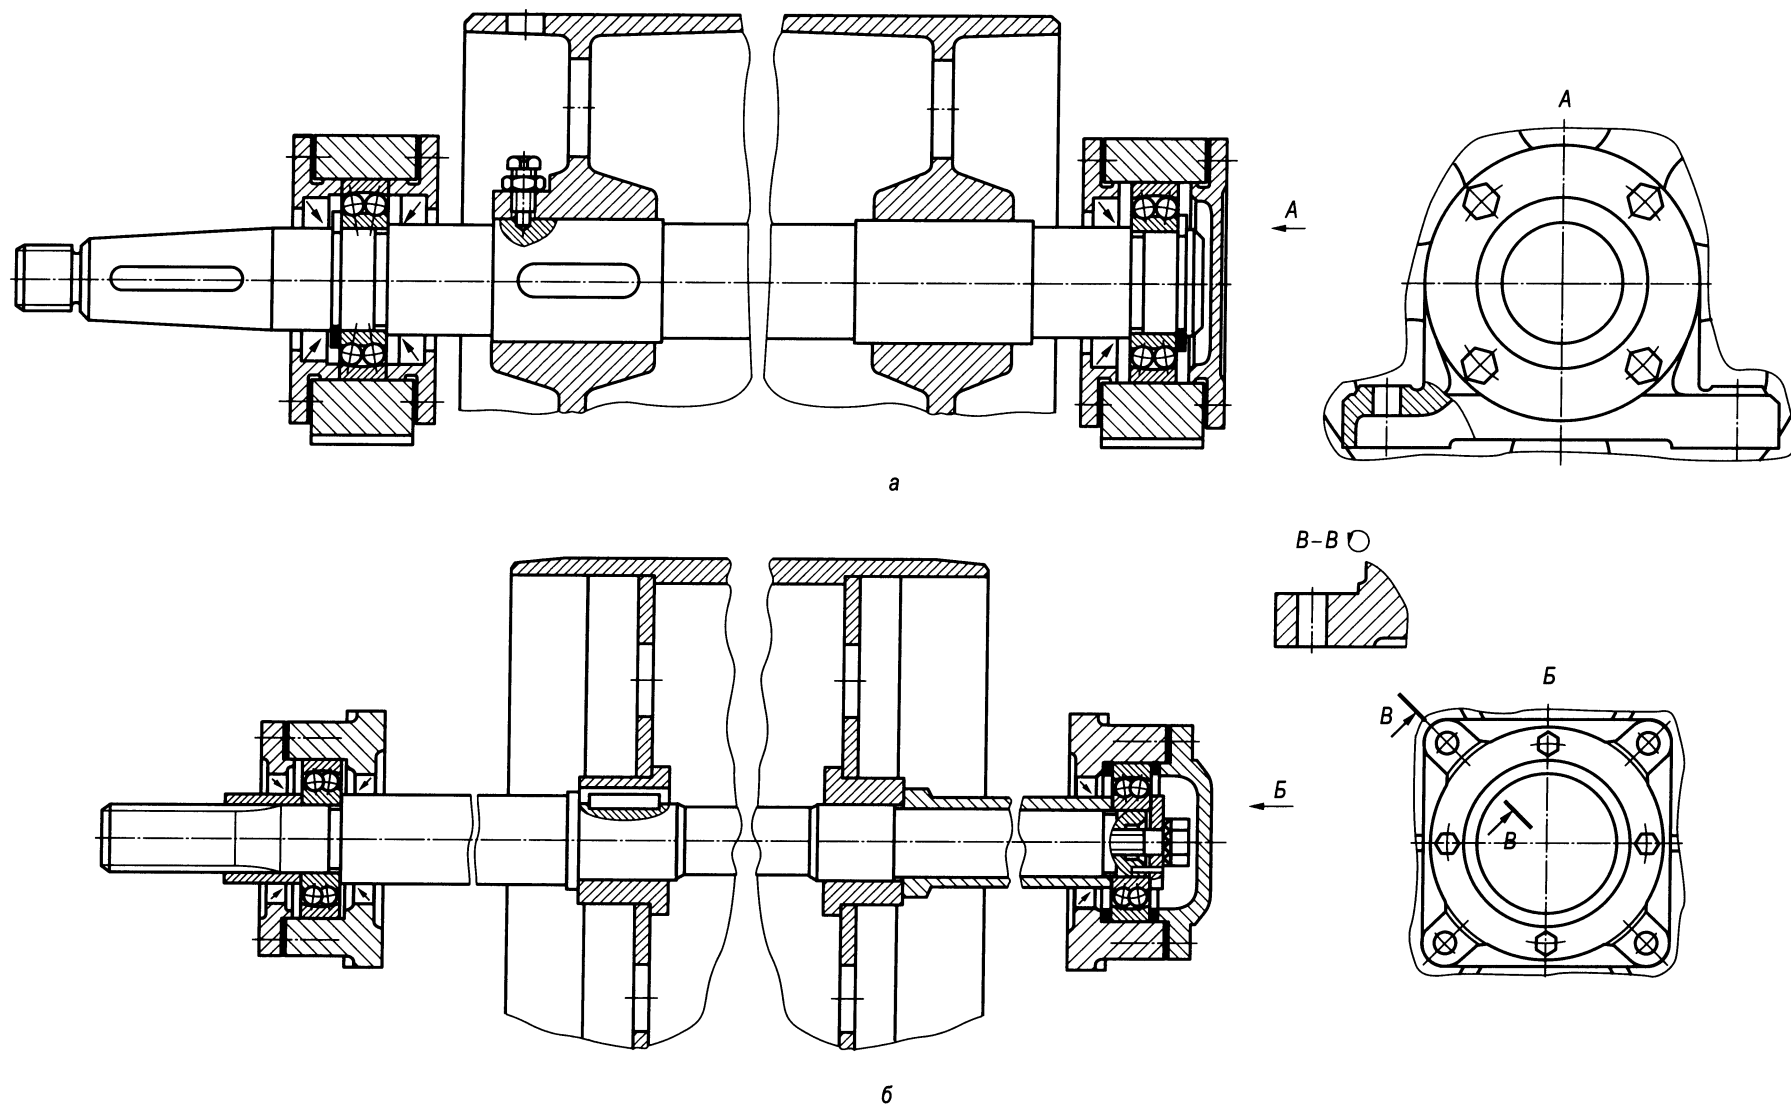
Вал приводной с литым (а) и сварным (б) барабаном
